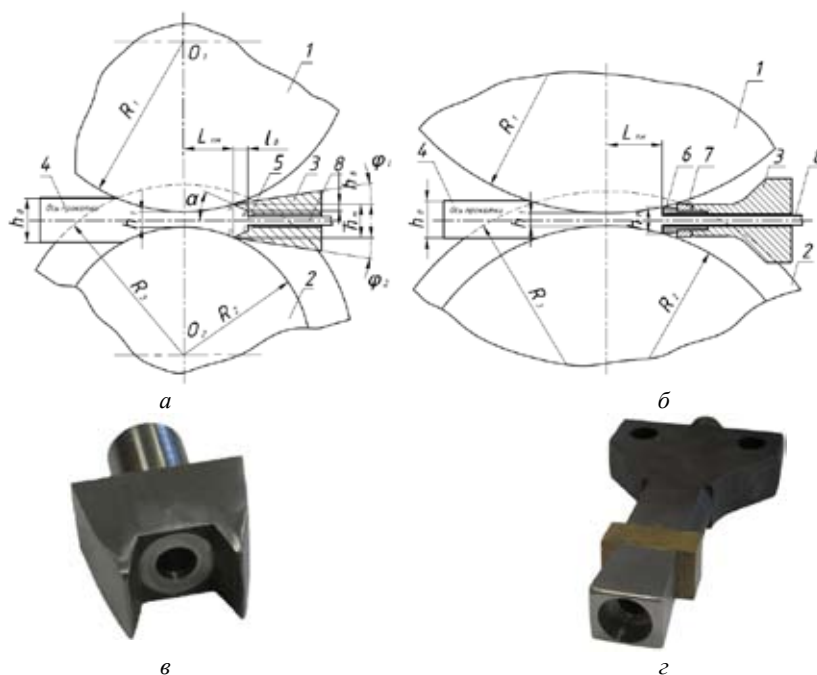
Устройства для совмещенной прокатки и прессования (СПП) по патенту РФ № 138590 (а) и РФ № 139085 (б) и вид матричного инструмента (в, г): 1 – валок с выступом; 2 – валок с канавкой; 3 – матрица; 4 – заготовка; 5 – трапецидальная выемка; 6 – калибрующая вставка; 7 – антифрикционная вставка; 8 – изделие
